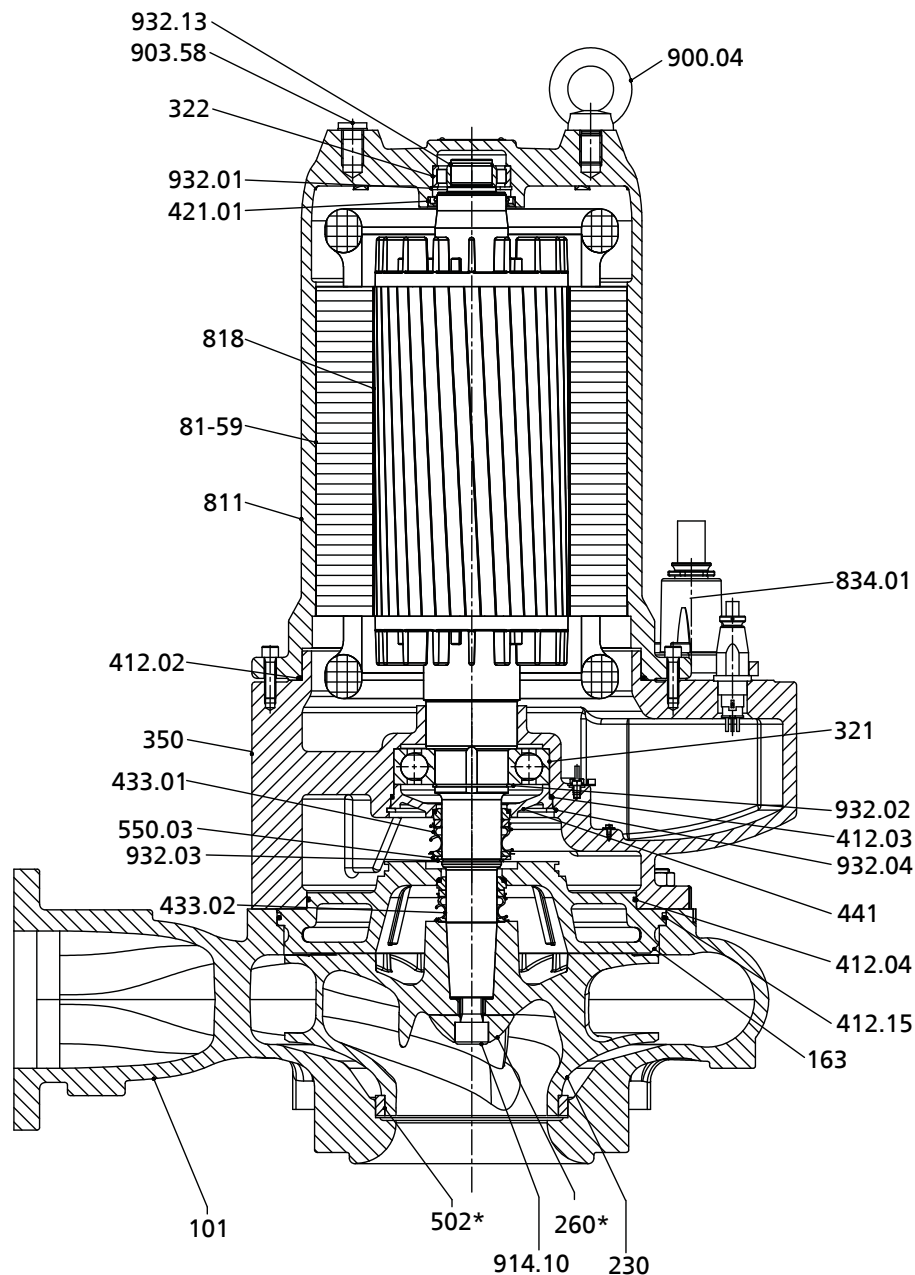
Сборочный чертеж Amarex KRT, тип двигателя 3
